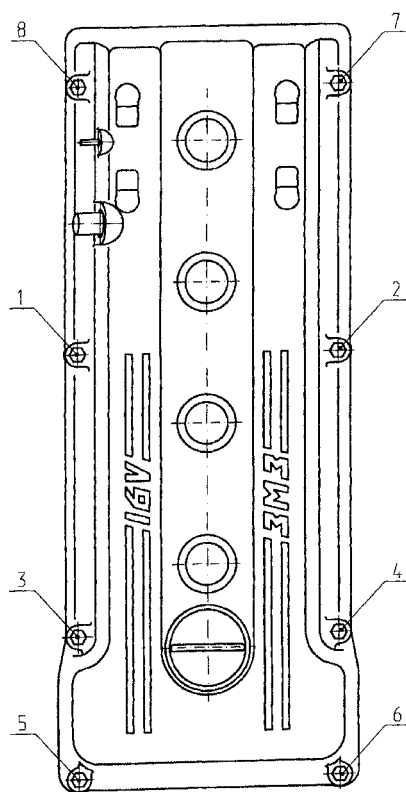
Последовательность затяжки болтов крепления крышки клапанов
